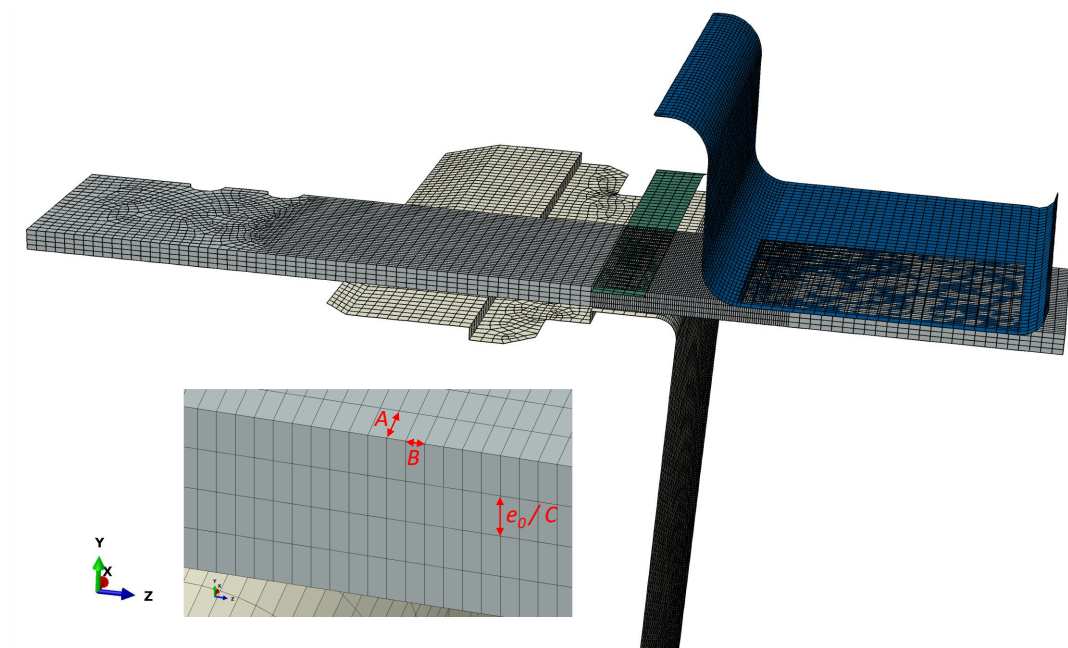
Maillages de l'éprouvette avec le maillage initial ($A = 0,2 \text{ mm}$; $B = 0,08 \text{ mm}$; $C = 4$ éléments) et des outils et définition des dimensions de l'élément dans la largeur A et la longueur B de l'éprouvette, et indirectement la dimension dans l'épaisseur par le nombre d'élément dans l'épaisseur C
